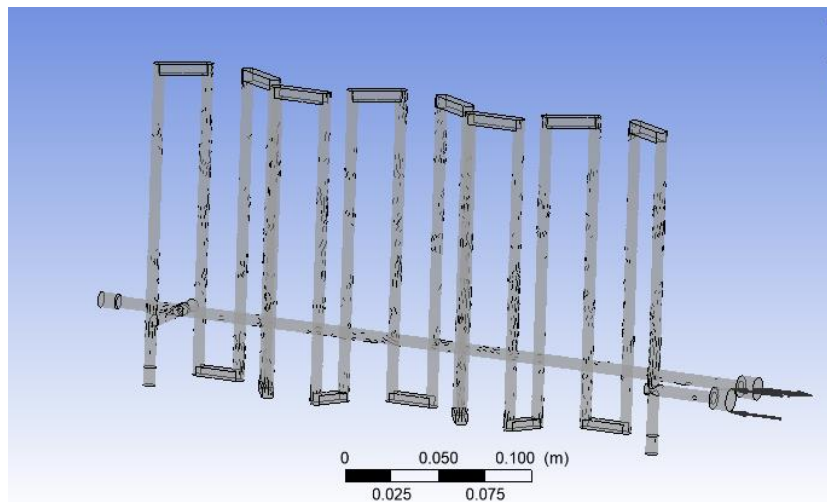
Molde en formato CAD (Elaboración propia)
